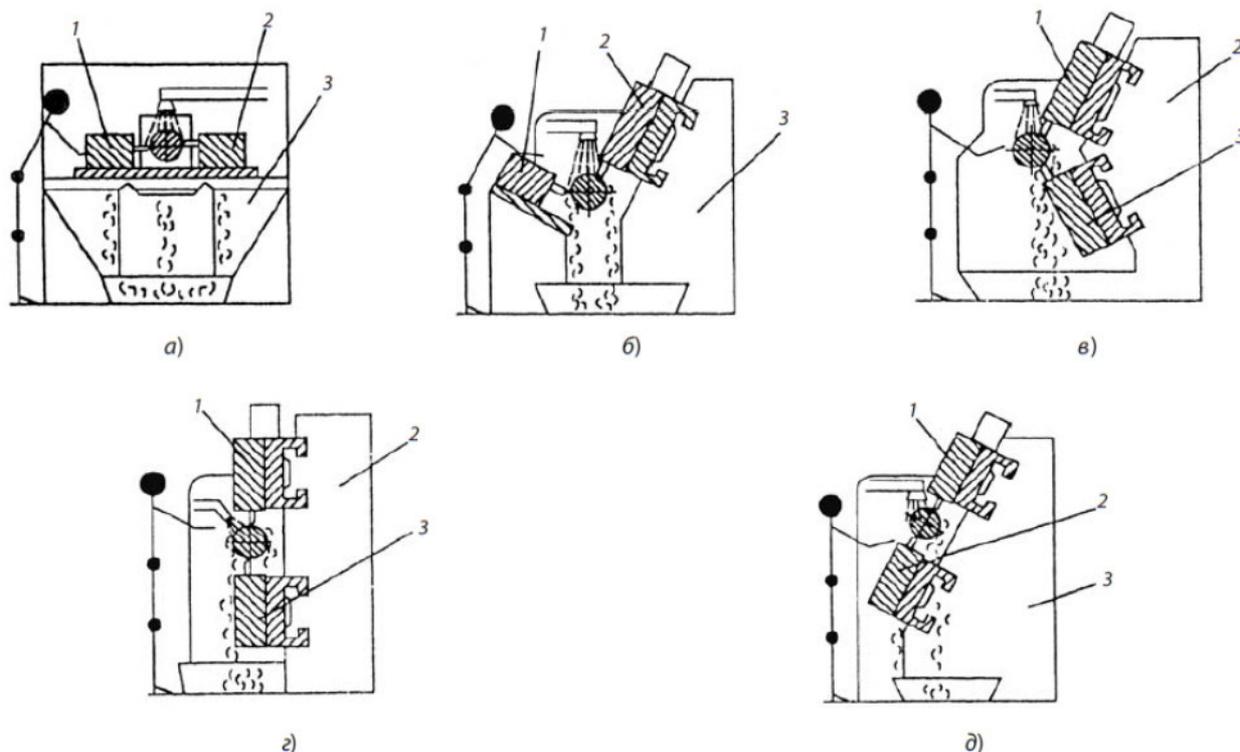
Варіанти компоновок станини та супортів в токарних верстатах: а – горизонтальна; б – двостороння похила; в – похила з розташуванням одного супорту в нижній частині станини; г – вертикальна; д – похила з розташуванням супортів паралельно один одному
